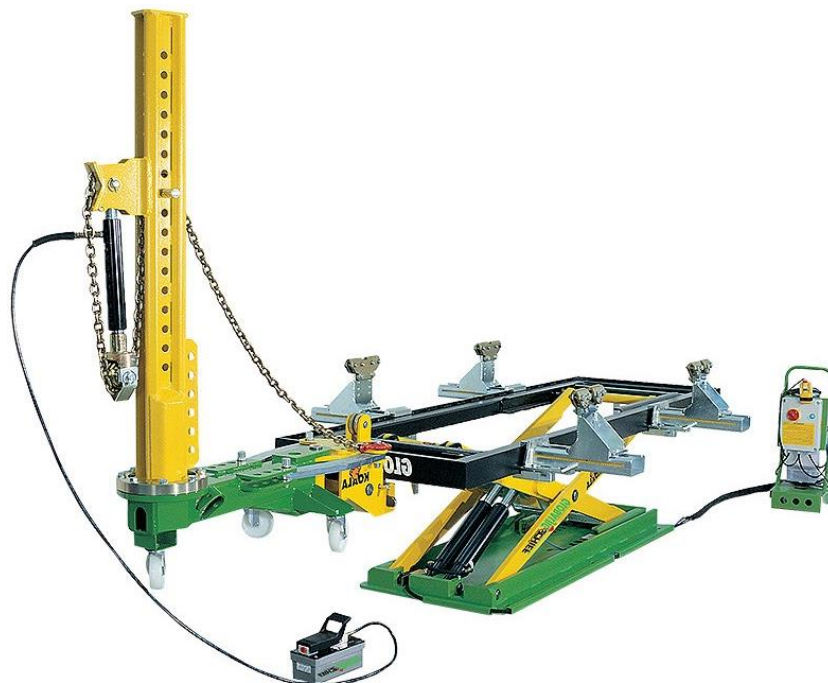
Стенд для правки кузова GLOBALJIG KOALA
